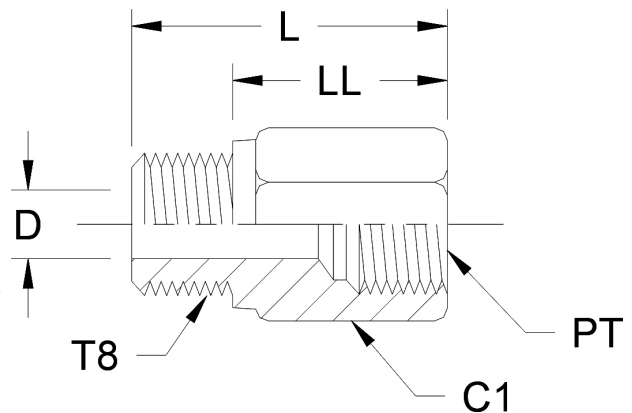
Diagrama dimensional del Adaptador de conversión - Métrica a NPTF
